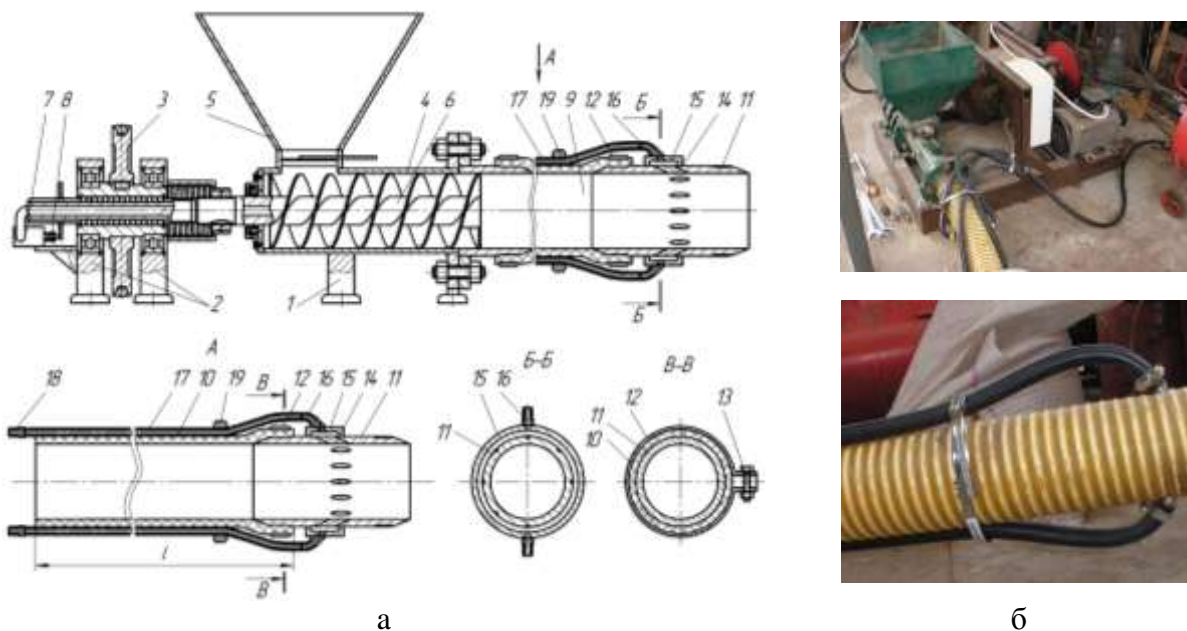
Конструктивна схема (а) та загальний вигляд (б) пневмо-шнекового транспортера з під'єднаними шлангами живлення до гнучкого кожуха
